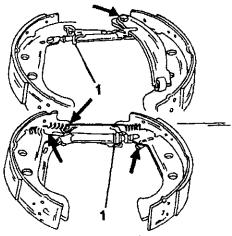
Сборка тормоза Bendix. Для правильного подсоединения пружин особое внимание уделять местам, указанным стрелками. Установочное колесо разместить так, как показано на рисунке.
